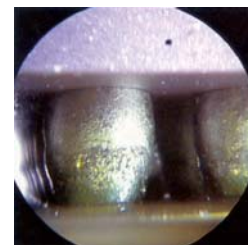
Шероховатость поверхности вывода BGA – дефект или норма?
